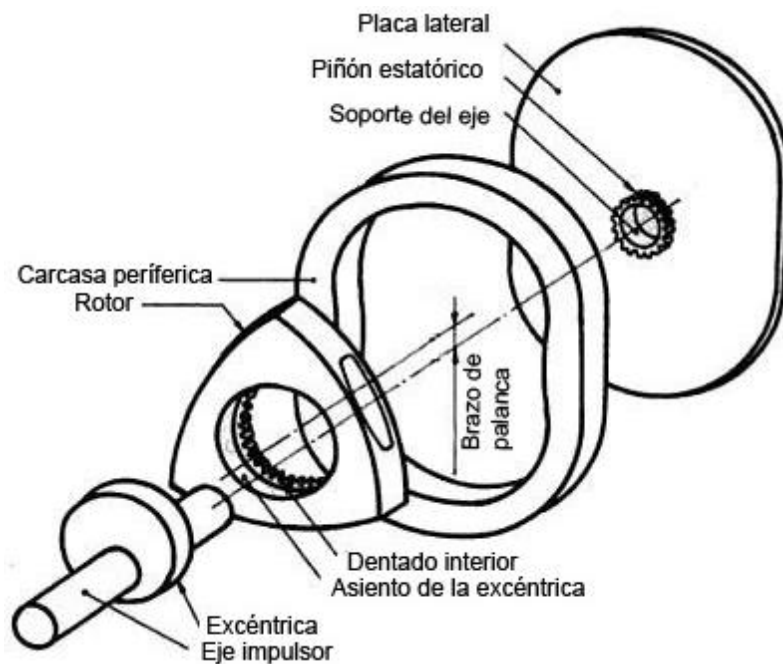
Elementos principales del Motor Rotativo Wankel.
